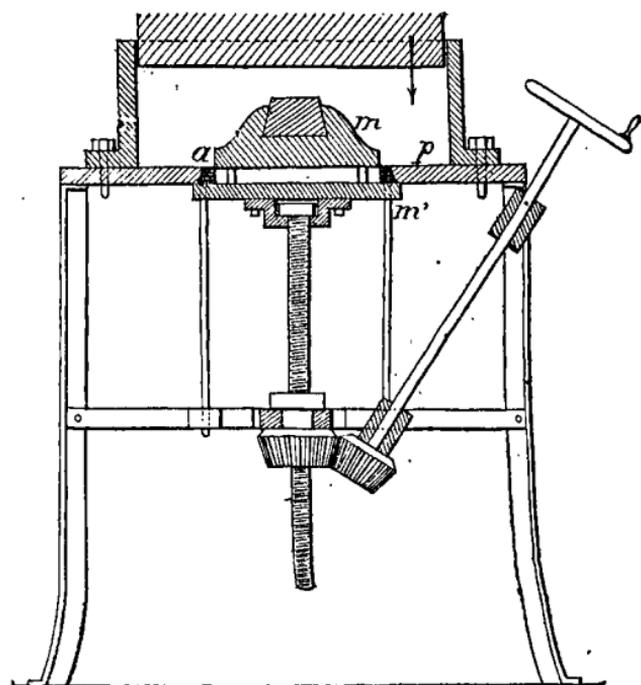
Machine à démouler. — *m*, modèle mobile fixé à la plaque *m'*; *p*, peigne complété par la garniture en alliage fusible *a*.
